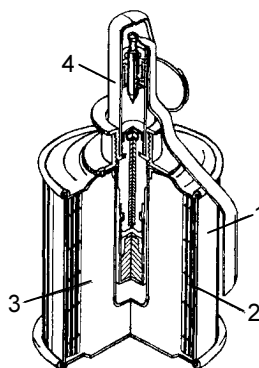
Граната РГ-42: 1 - корпус; 2 - металева стрічка; 3 - розривний набій; 4 - запал
